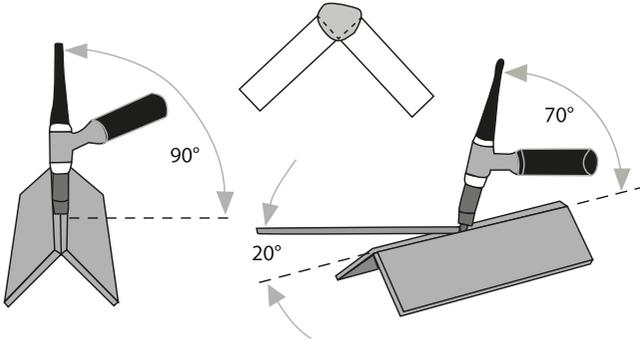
Положення пальника під час виконання зварювання кутового з'єднання.
